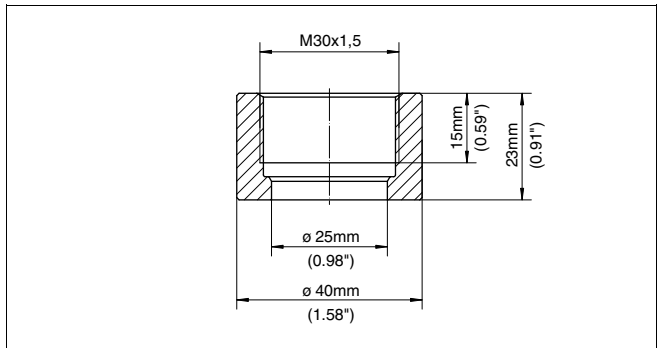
Medidas racor soldado M30 x 1,5 para la caja de entrada de pasta
